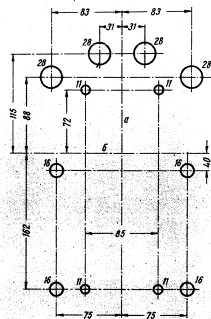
Сверление отверстий для установки на изоляционных плитах контакторов типа КТИ 524 и КТИ 544 с задним присоединением
